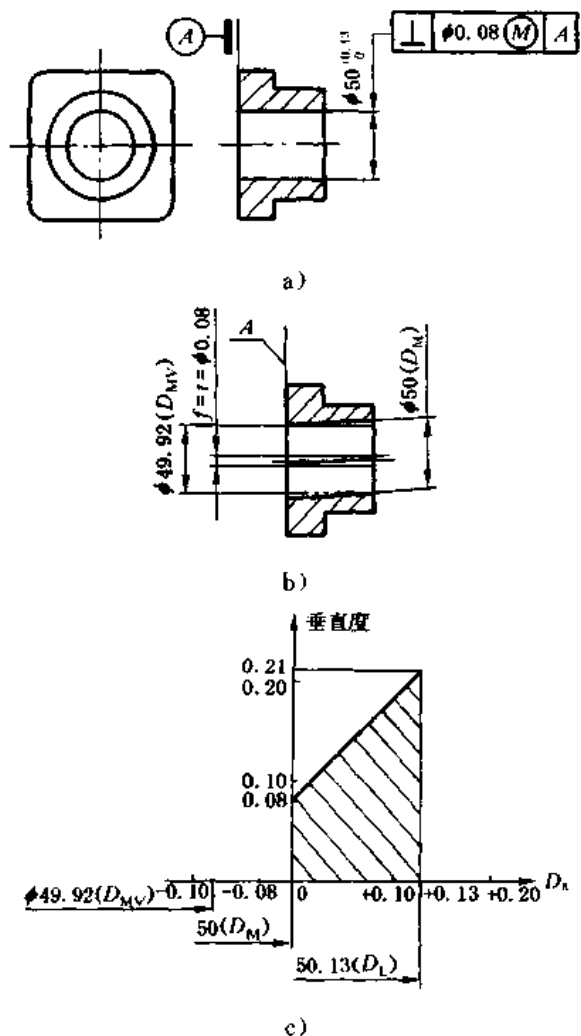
轴线垂直度公差采用最大实体要求
